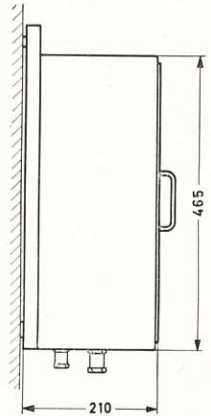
mit Gehäuse für Wandaufhängung 90zBW
